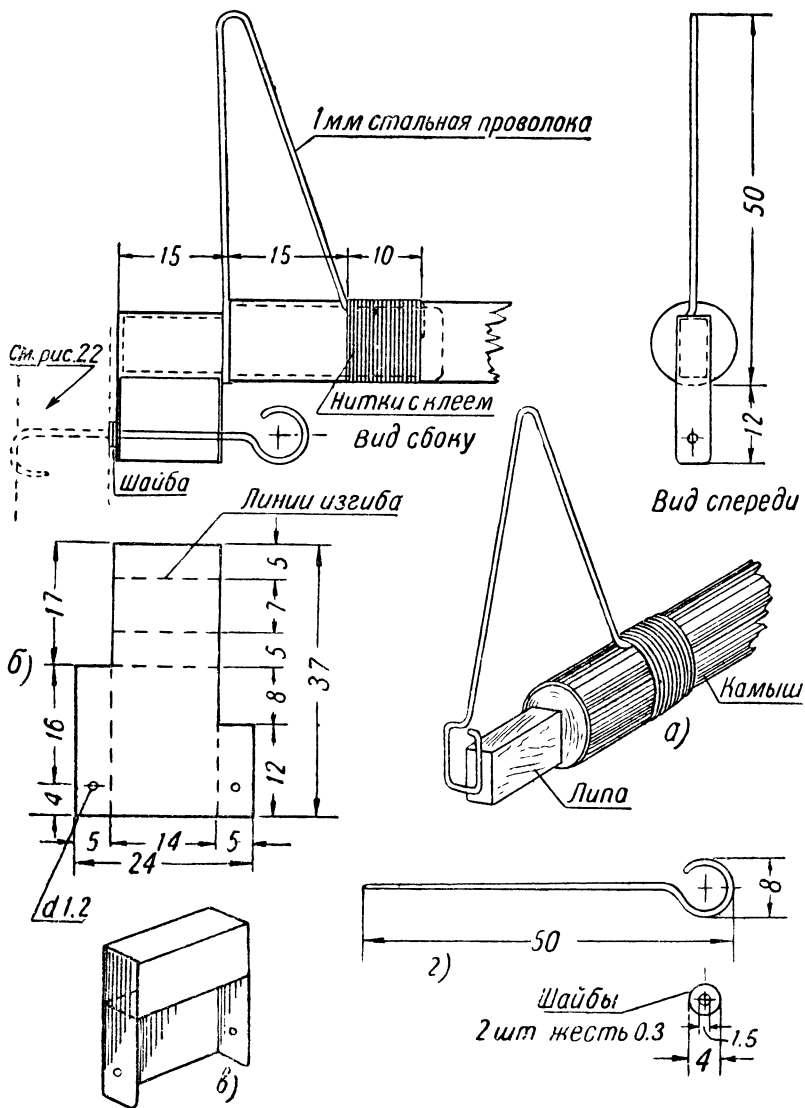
Подшипник, сбрасыватель и передняя бабышка: а) общий вид сбрасывателя и передней бабышки; б) развертка подшипника; в) общий вид подшипника; г) ось винта и шайбы
